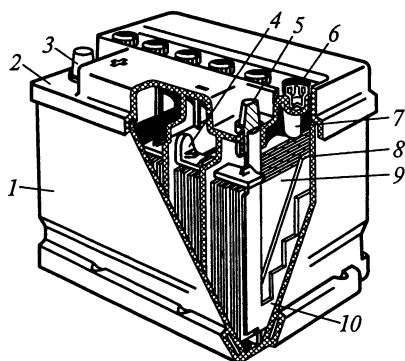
Аккумуляторная батарея: 1 — корпус; 2 — крышка; 3, 5 — выводы; 4 — мостик; 6 — пробка; 7 — индикатор; 8 — сепаратор; 9, 10 — пластины
